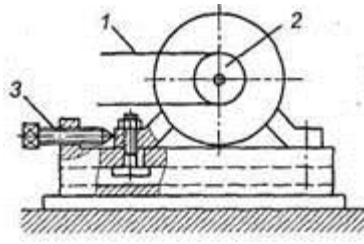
Регулировка натяжения ремня перемещением двигателя: 1 — ремень; 2 — шкив; 3 — натяжное устройство
